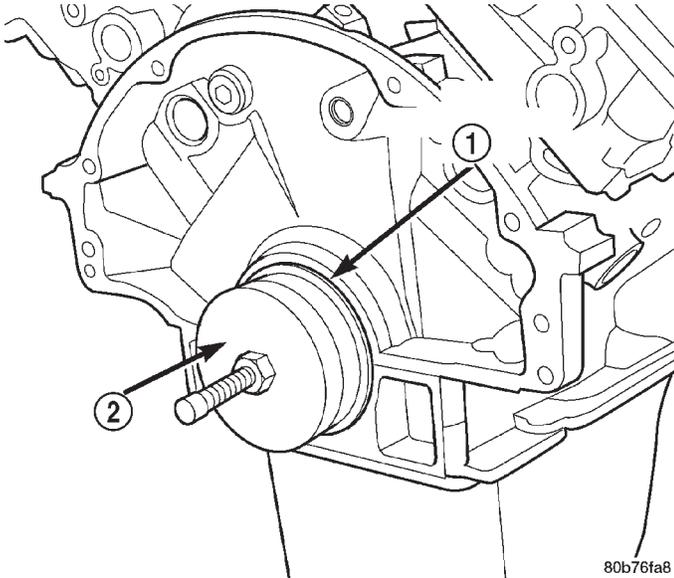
Ausbau des hinteren Kurbelwellendichtrings
